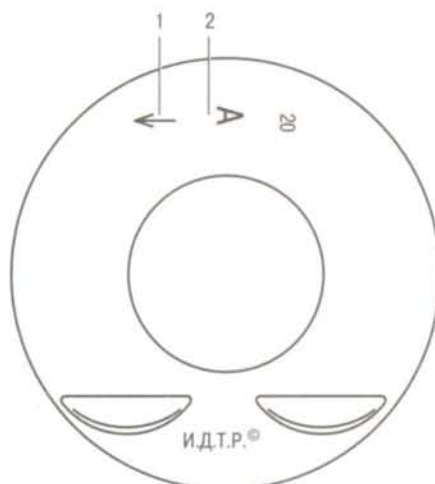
Маркировка поршня: 1 – указатель передней части двигателя; 2 – класс поршня
